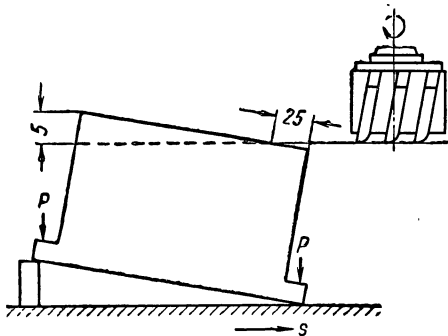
Установка детали при обработке на вертикально-фрезерном станке
